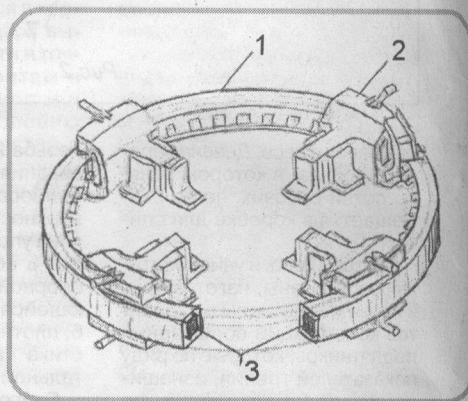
Кольцевой накопитель с супермаховиком: 1 — вакуумированный корпус, 2 — магнитные активные опоры, совмещенные со статором линейного двигателя, 3 — кольцевой супермаховик из сверхпрочного волокна.
